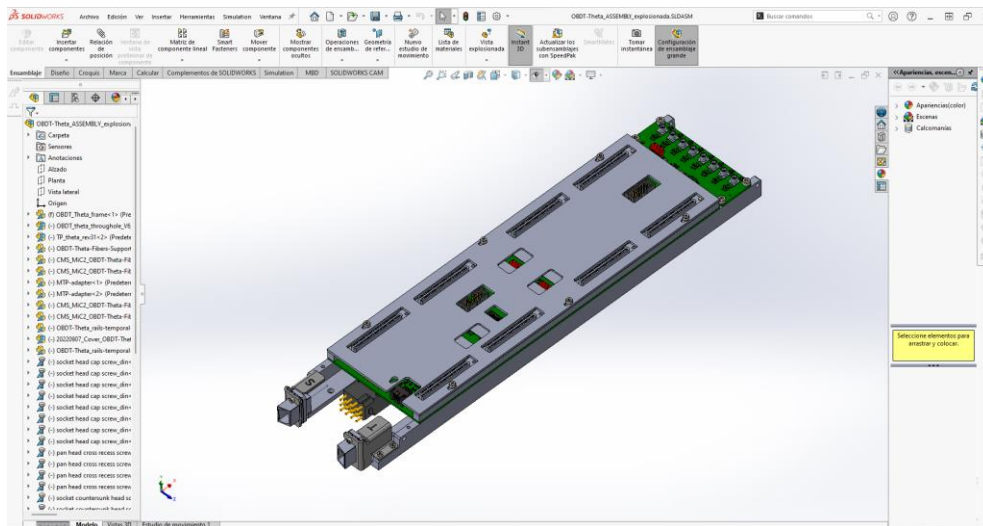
Vista en perspectiva del ensamblaje 3D de la OBDT-Theta en Solidworks.
